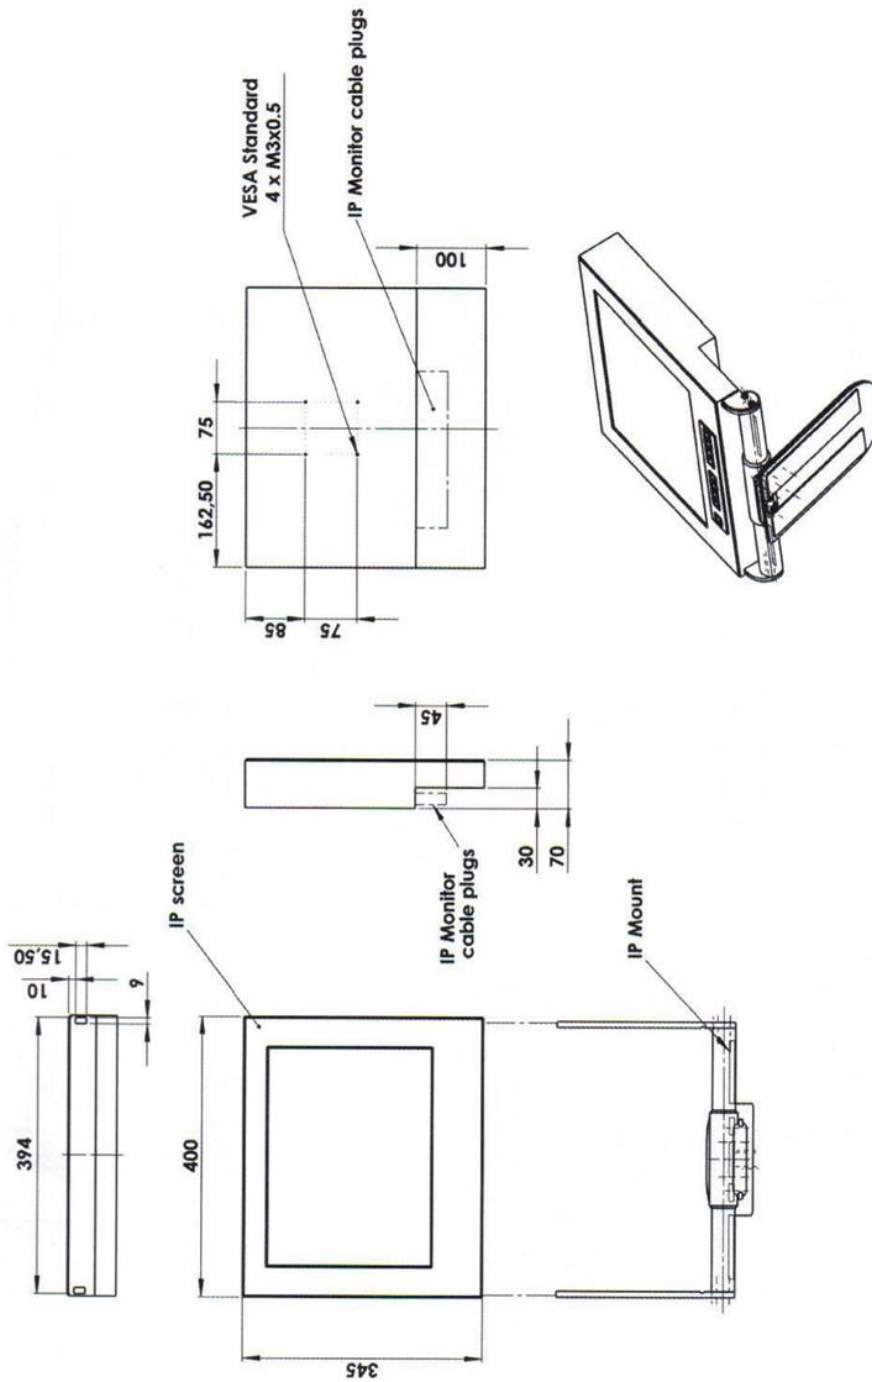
Dimensiones del panel de interfase (dimensiones en mm)
